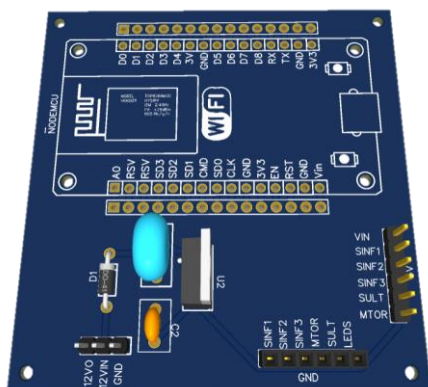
Vista 3D superior del diseño PCB del módulo principal.
